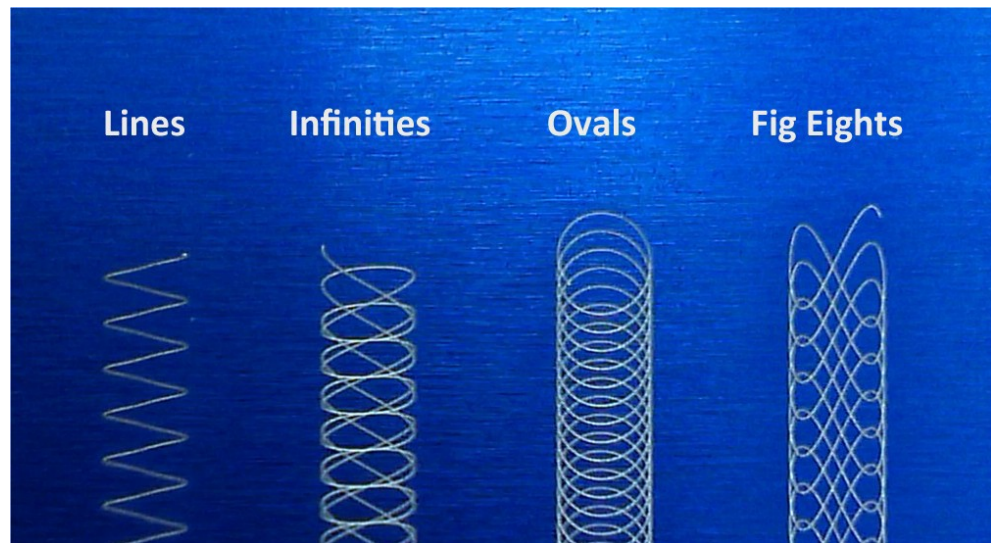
Примеры траекторий движения фокусного пятна при лазерной сварке с осцилляцией фокусного пятна (англ., Laser Wobble Welding) © Polaris Laser Wobble Technology.
